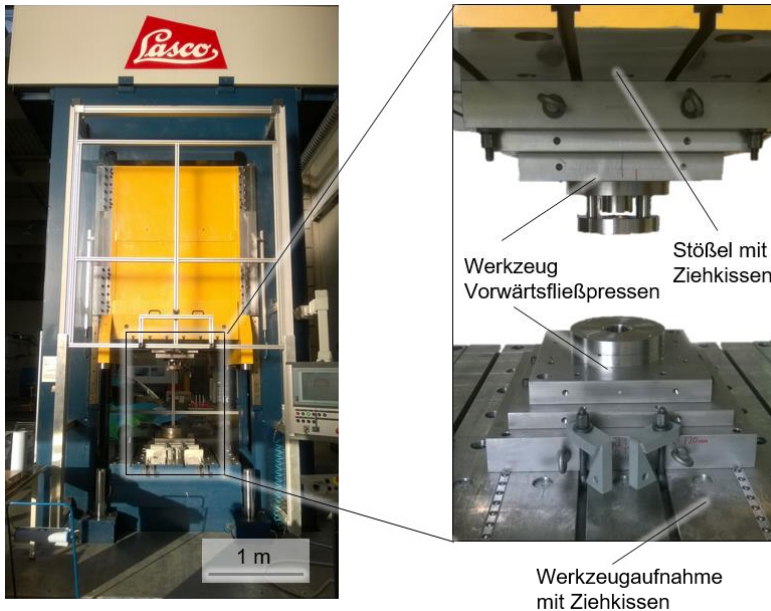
Presse des Typs Lasco TZP 400/3 mit einer Nennkraft von 4000 kN und eingebauten Werkzeug zum Vorwärtsfließpressen
